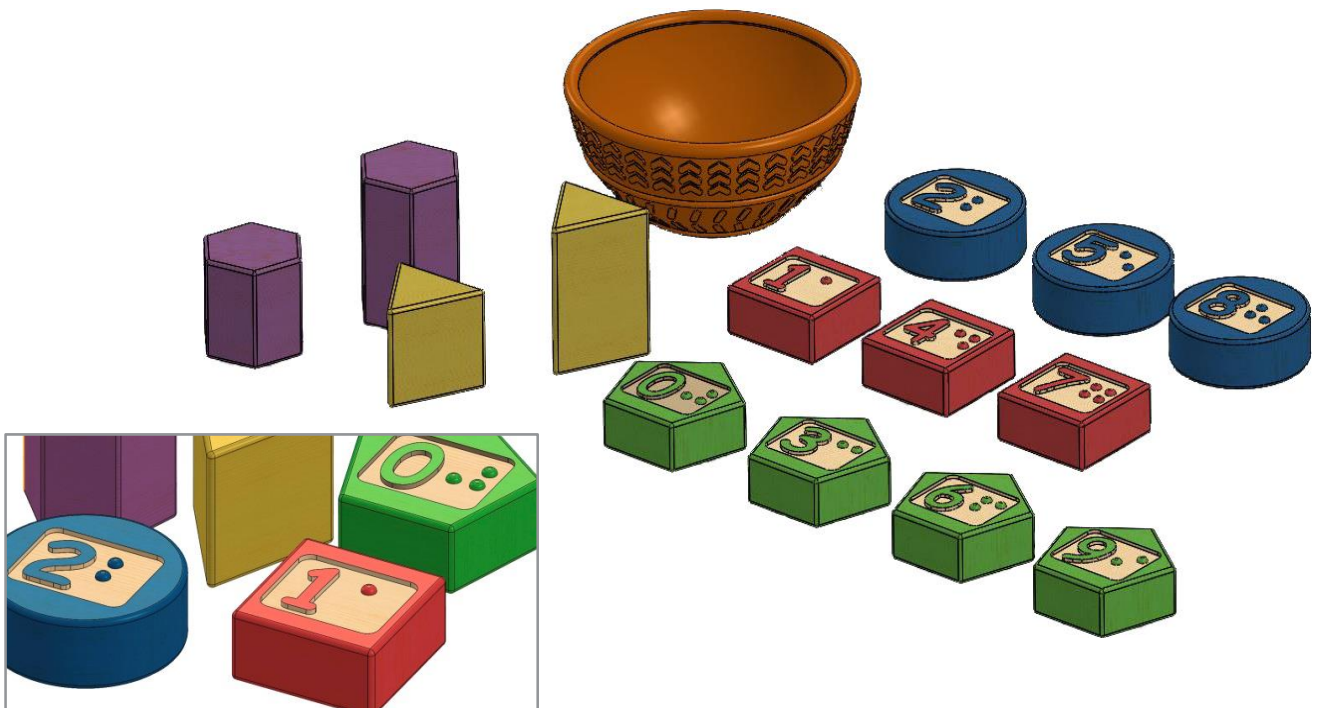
Piezas con color y a la izquierda detalle de la beta tras la coloración
